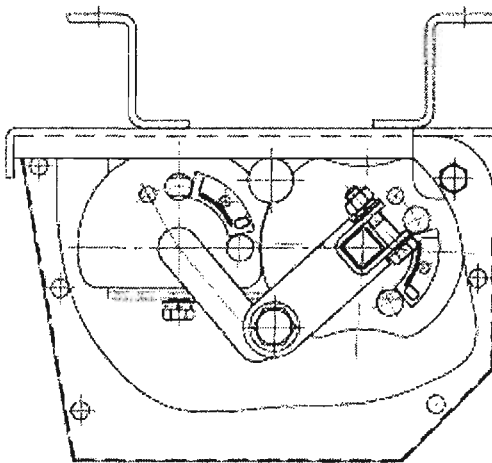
Привод ПР СЭЦ-01 УХЛ1
